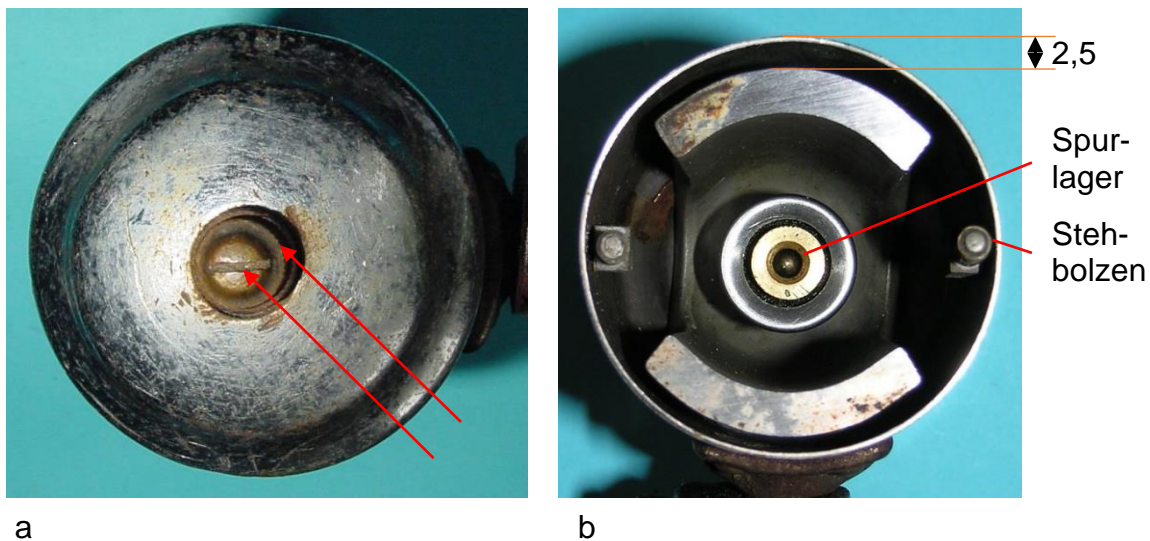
Ansichten: a) Boden mit durchgesteckter Lagerbefestigung und Öl-schraube, b) Zweipoliger Tulpenmagnet mit Spurlager im Gehäusetopf
